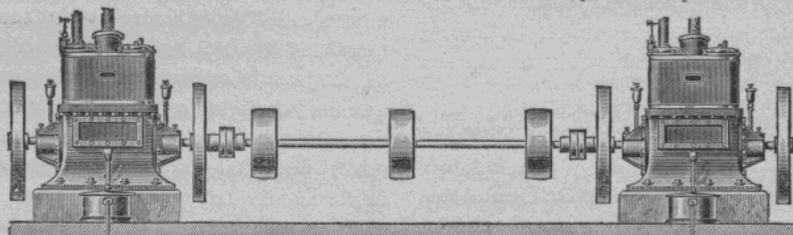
Accouplement de 2 machines pour conduire des dynamos.
